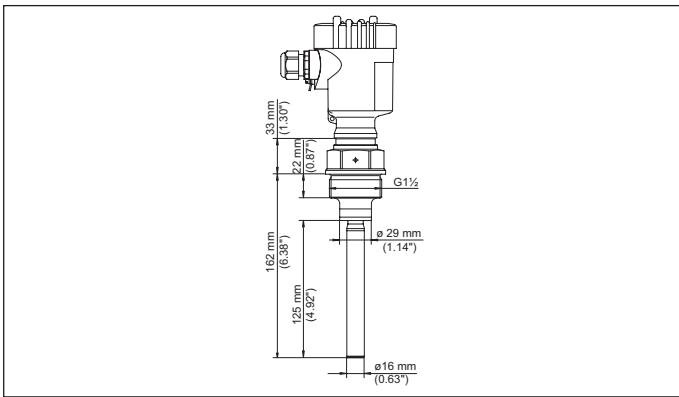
VEGAVIB 61 - Gewindeausführung G1½
